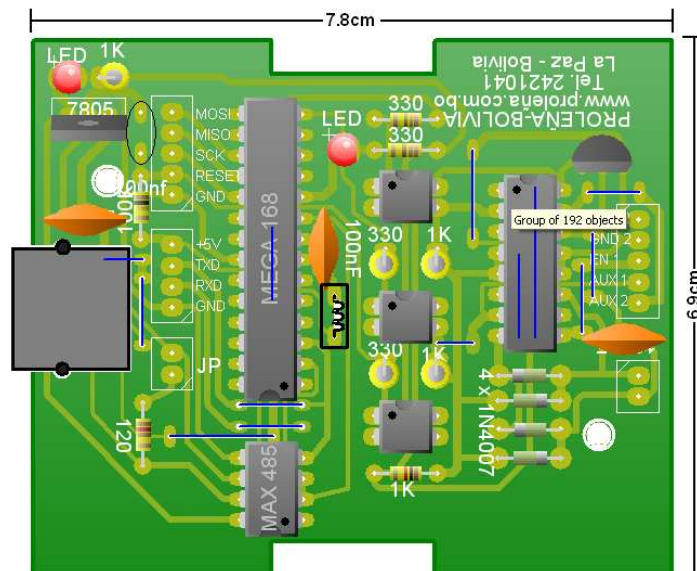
PCB ACABADO PERIFÉRICO RMS/DC
